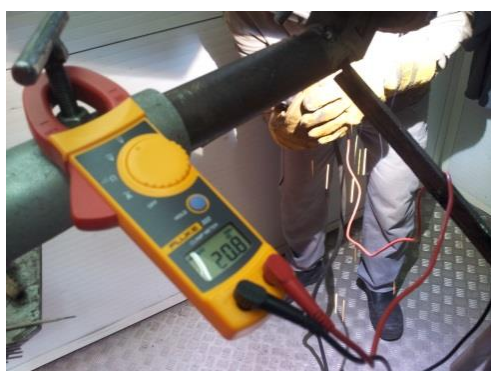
Medição da tensão de soldadura no processo SER
